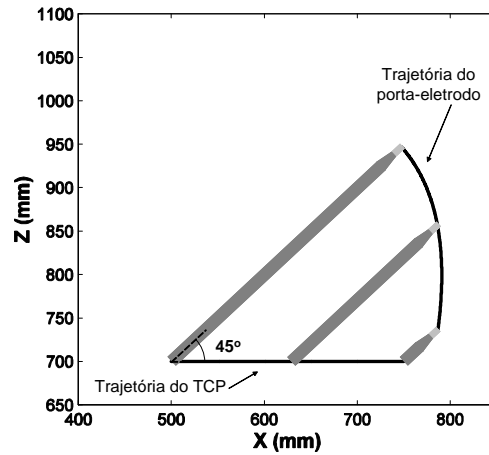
Trajetórias do TCP e do porta-eletrodo para soldagem com ângulo de  $45^\circ$ .
